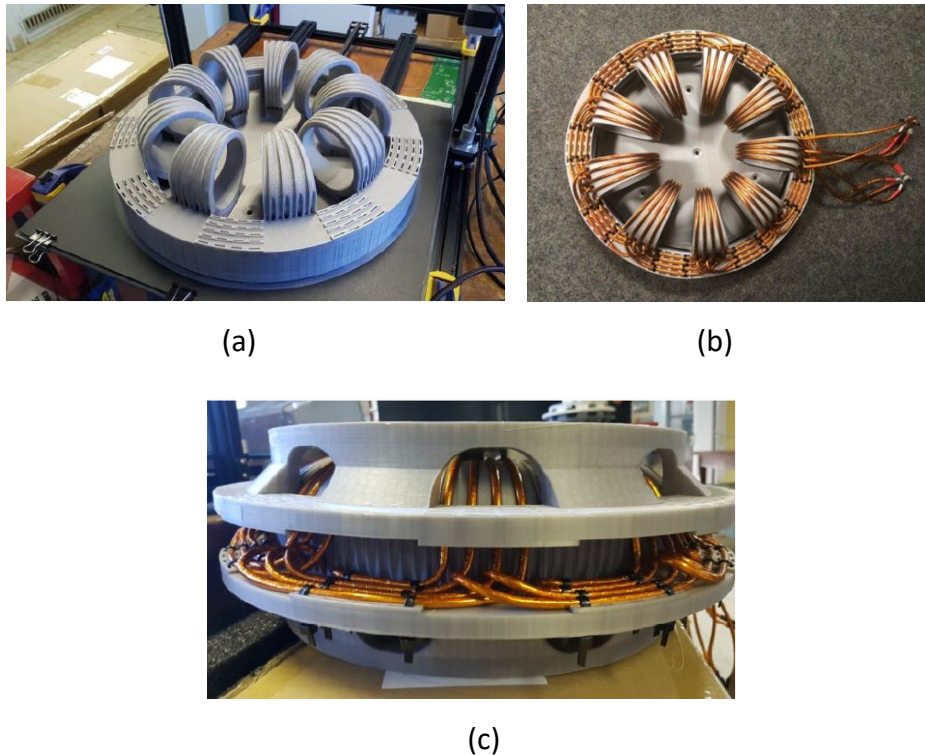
Prototype du coupleur électromagnétique démontable.
